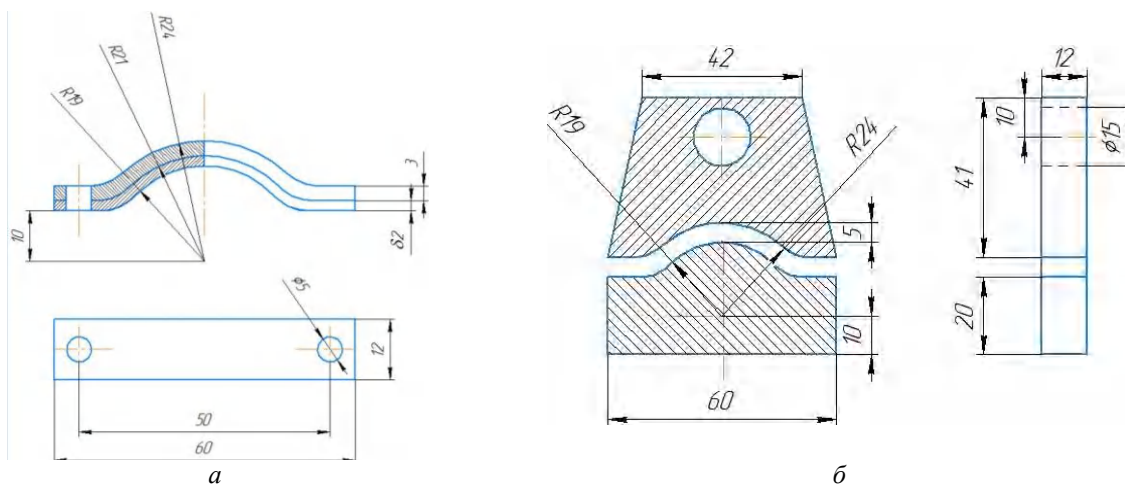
Образец для испытания на износ (а) и пресс-форма из стали 50ХГФА для формообразования образцов (б)
